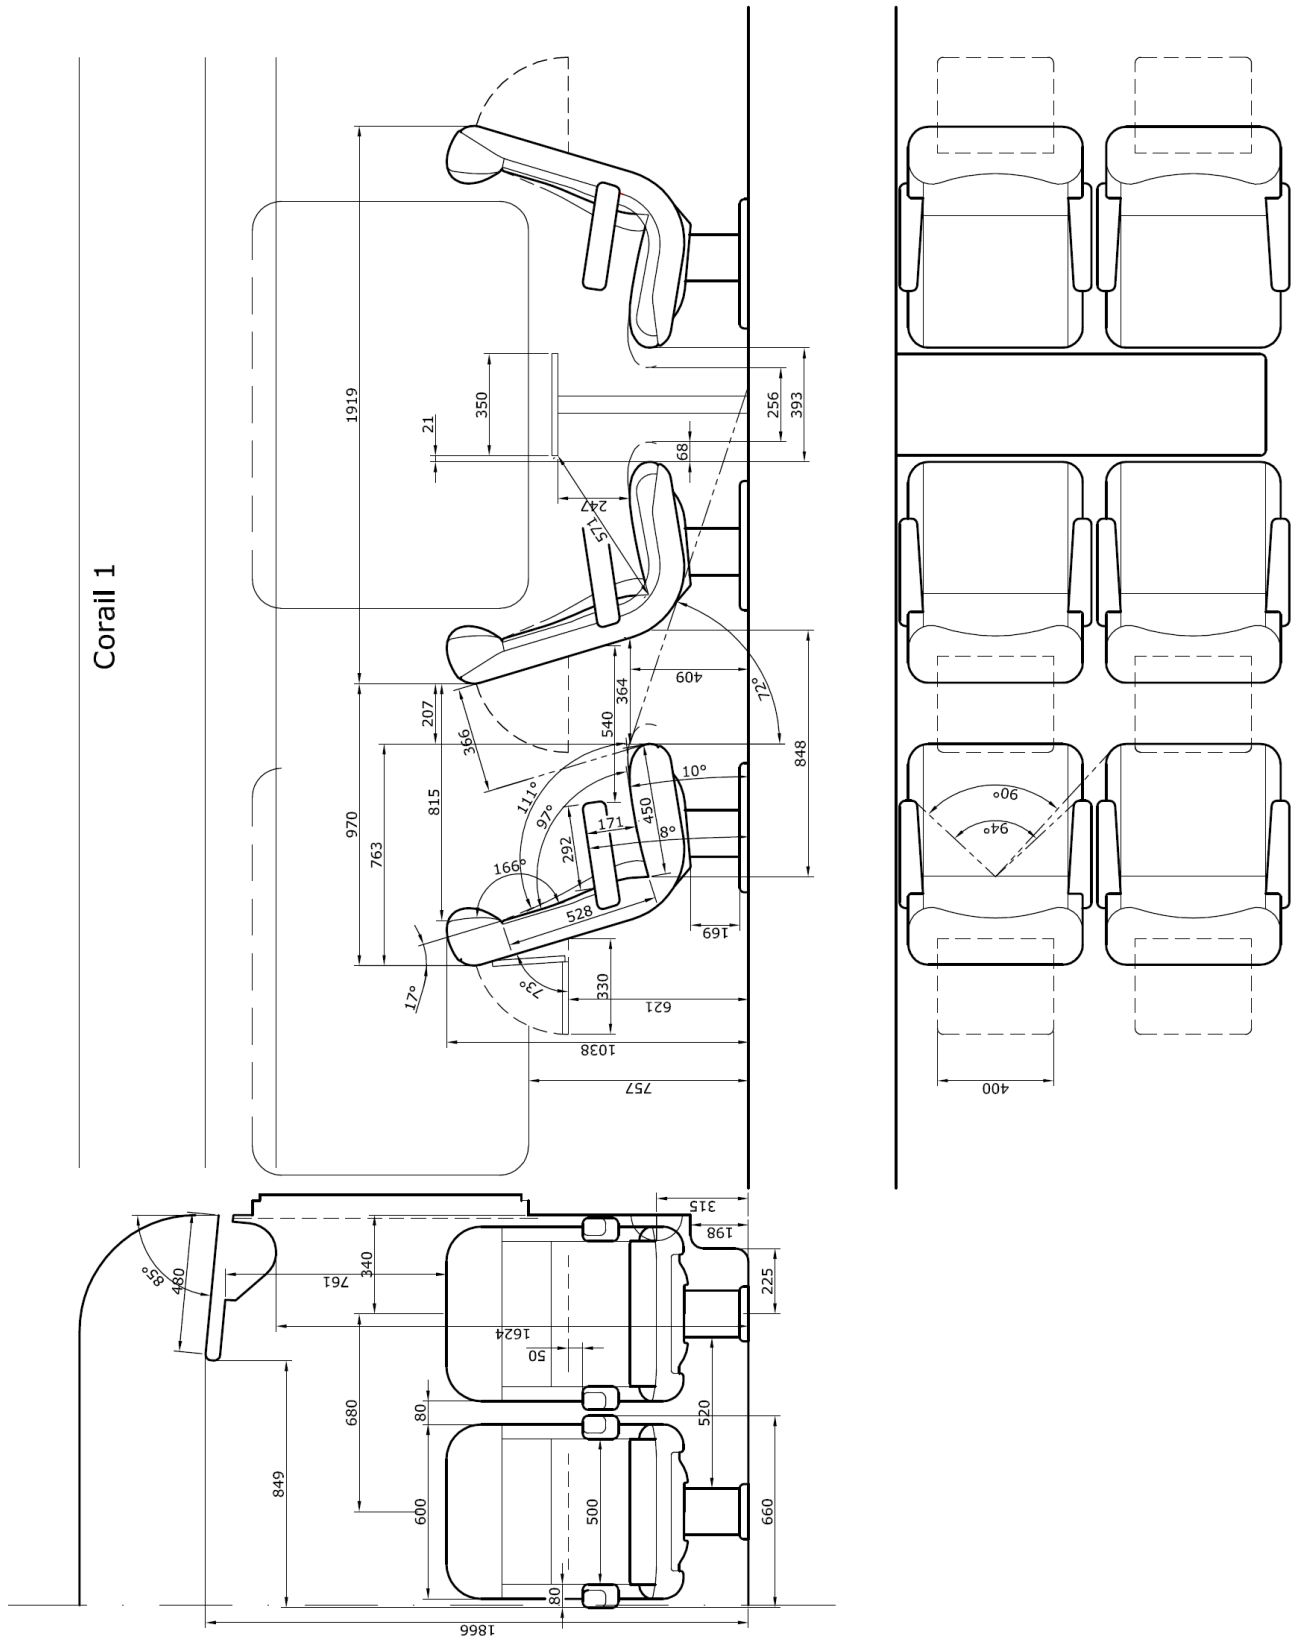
Espaço pessoal no salão de passageiros Corail 1 (Corail de 1ª classe) levantamento dimensional. Unidades em mm. Vista transversal, vista longitudinal e vista de cima segundo Método Europeu de Representação.
